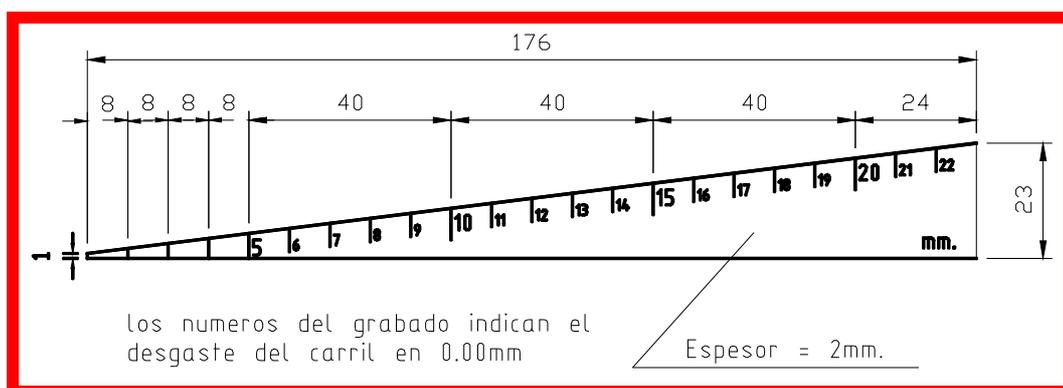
b.: Regla escalada para desgastes de carril
